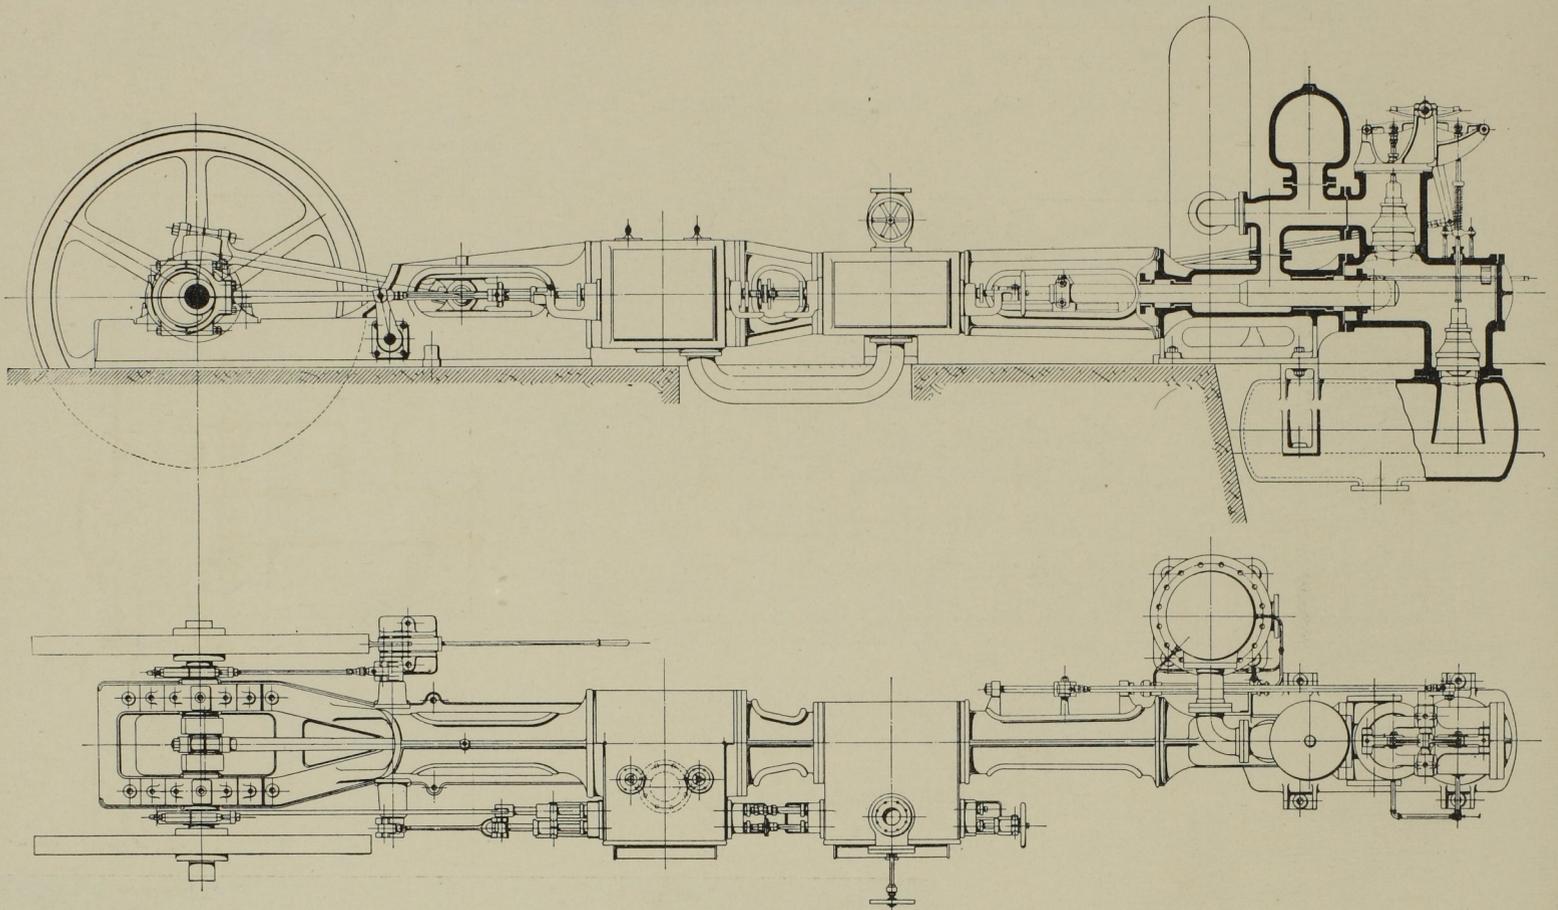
Seitenansicht und Grundriss. Massst. 1:48.
